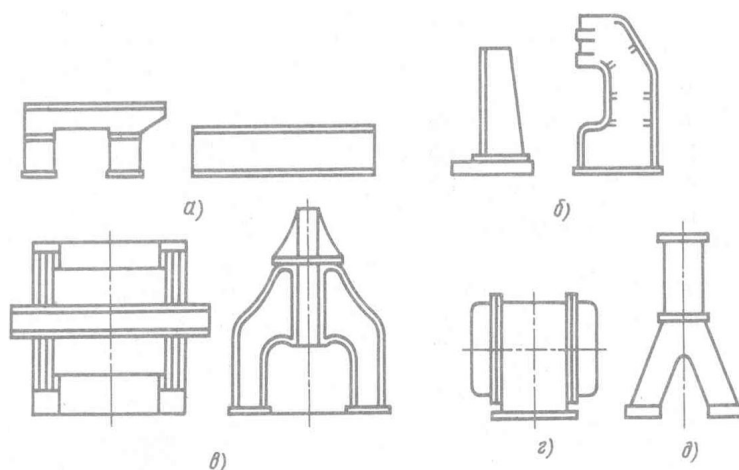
Корпусные детали (массивы): *а* – станины; *б* – стойки; *в* – портальные станины; *г* – кольцевая станина; *д* – блоки цилиндров
